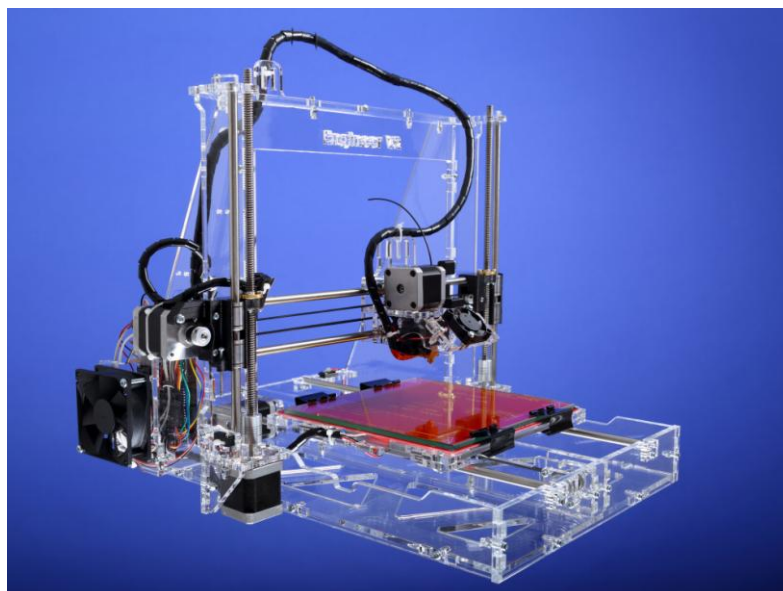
Экструзионный (FDM) 3D-принтер Engineer V2
